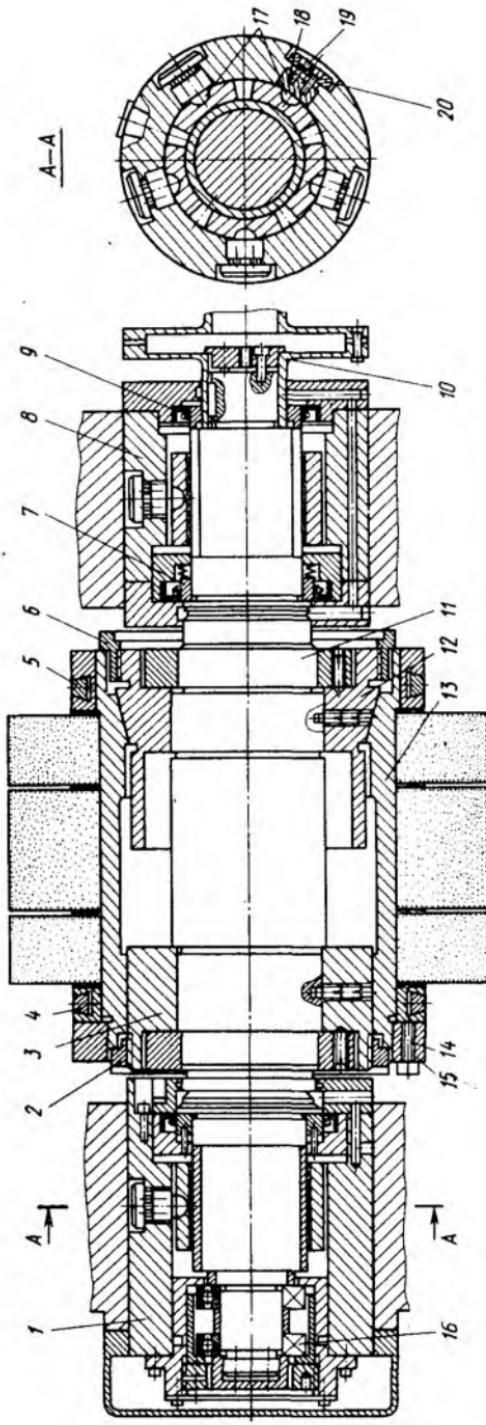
Шпиндель бесцентрово-круглошлифовального станка СЛ510
